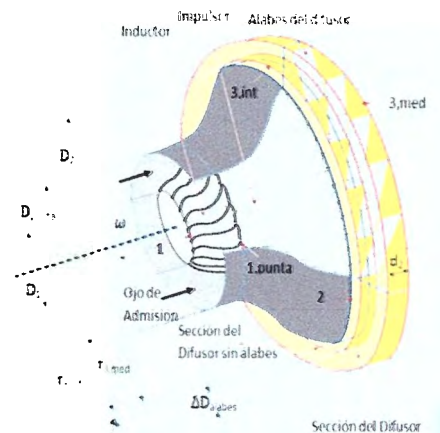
Conjunto compresor, en amarillo el estator, los álabes que compone el estator se alojan a una pequeña distancia del impulsor
